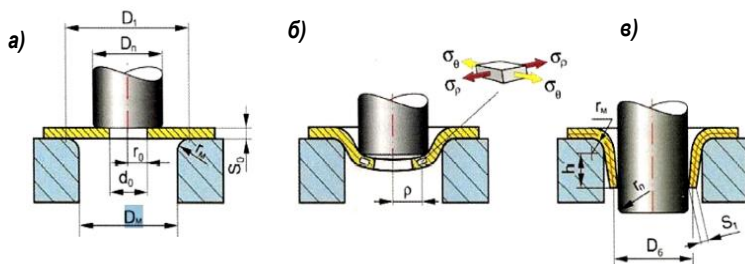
Схема формоизменения заготовки в процессе отбортовки
